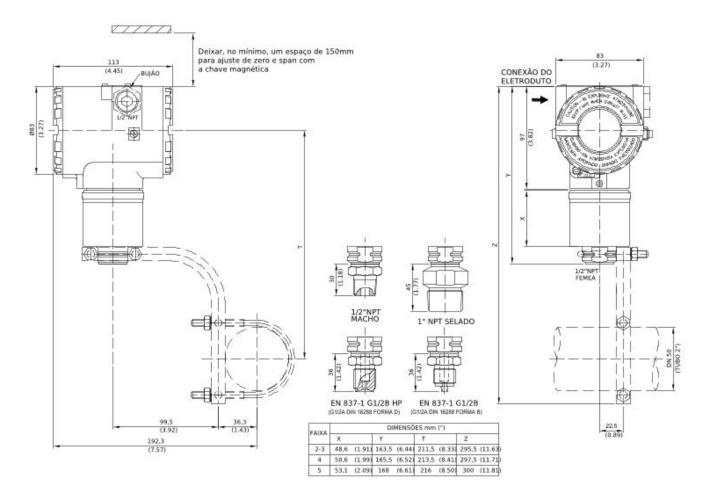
(a) – Desenho Dimensional e Posição de Montagem do LD292
